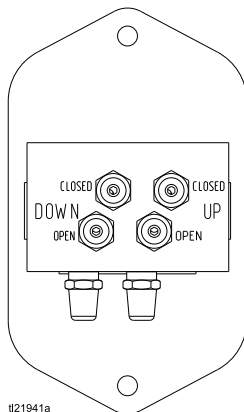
Schlauchanschlüsse am Magnetventilverteiler, zum Pumpeneinlassverteiler
